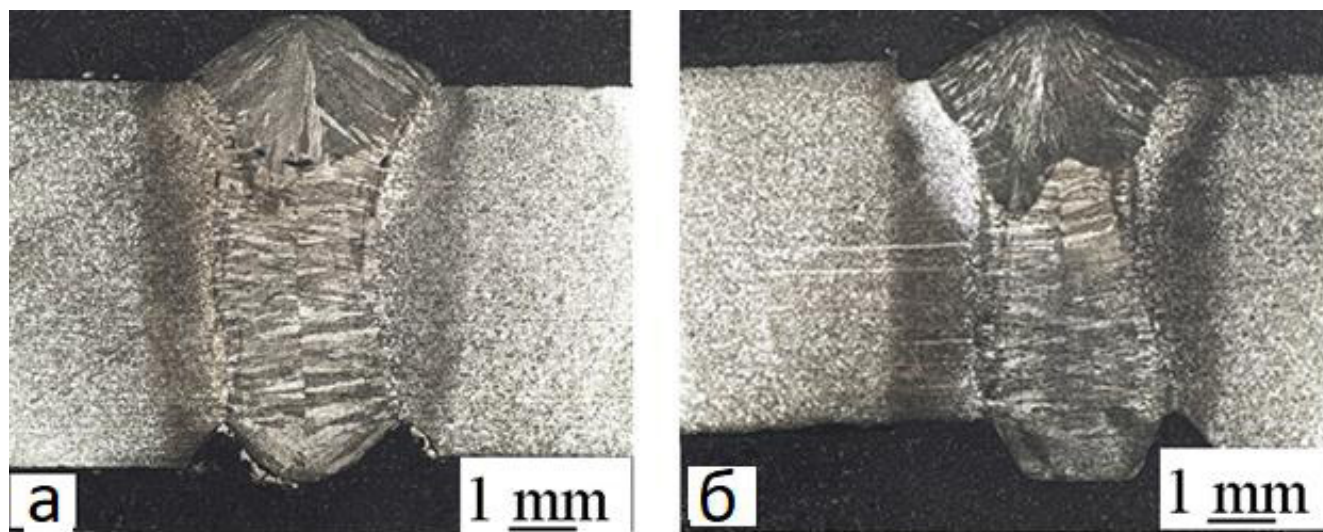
Сварной шов, полученный методом лазерной наплавки проволоки на поверхность образцов из трубной стали с мощностью лазерного излучения 2500 Вт (а), 4000 Вт (б).
